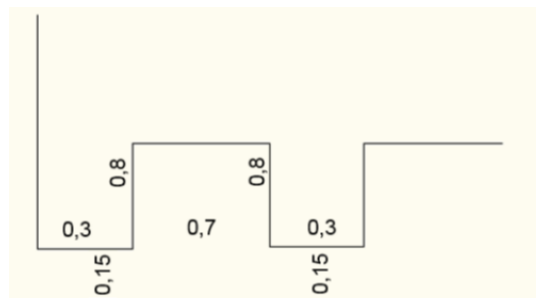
Dimensiunile (mm) unui etaj de etansare.
